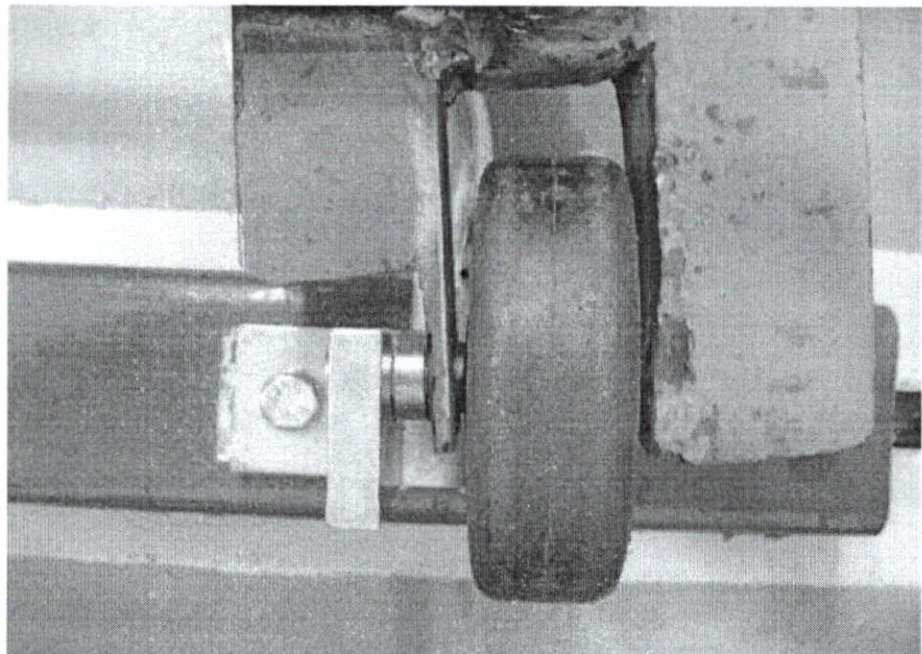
Lado esquerdo da amostra 2 após ensaio.
